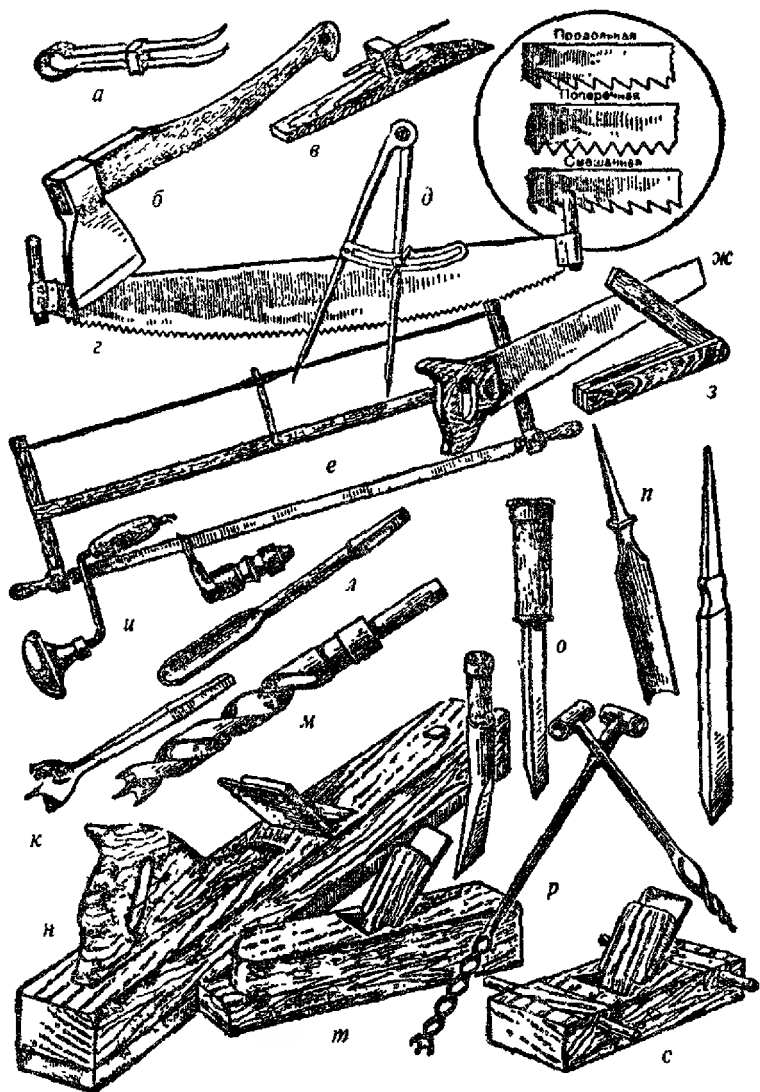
(1) Инструменты и приспособления для обработки дерева.
